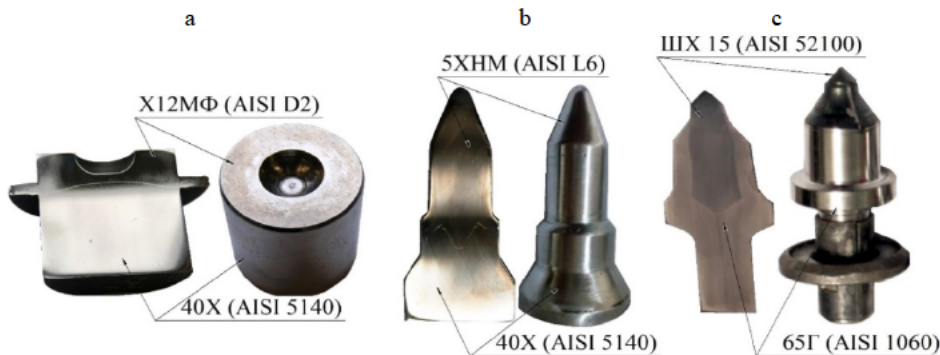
Детали-представители и их шлифы: а – вставка пуансона; б – прошивной пуансон; с – тангенциальный резец
